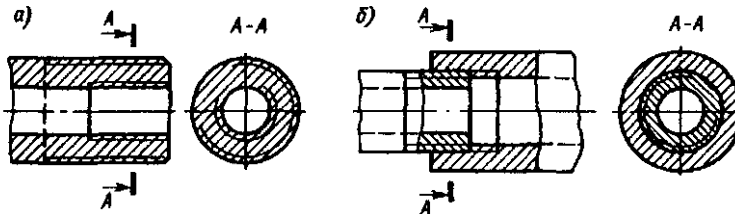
Изображение резьбы: *a* — во втулке с наружной и внутренней резьбой; *б* — в резьбовом соединении
